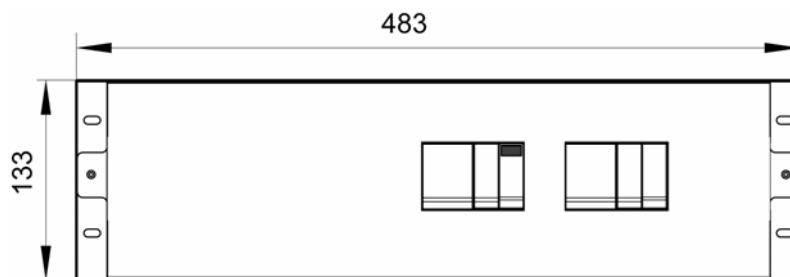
Внешний вид и габаритные размеры УЗИП - 1
